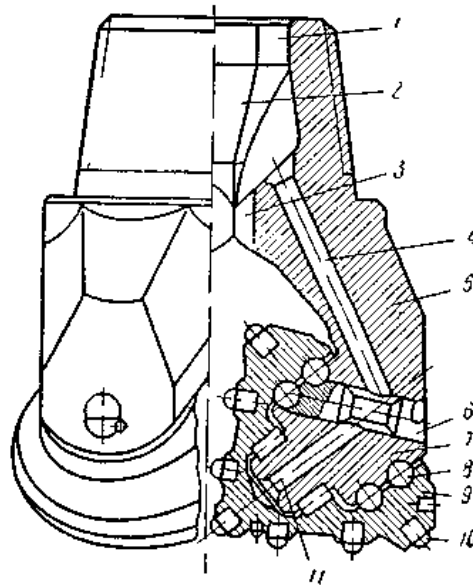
Три шарошечне долото для роторного буріння : 1 – внутрішня порожнина; 2 – підвідний канал; 3 – циліндричний промивний отвір; 4 – отвір для охолодження; 5 – лапа; 6 – палець; 7 – цапфа; 8 – підшипники; 9 – шарошка; 10 – зубчаті або суцільні вінці; 11 – отвір для охолодження
